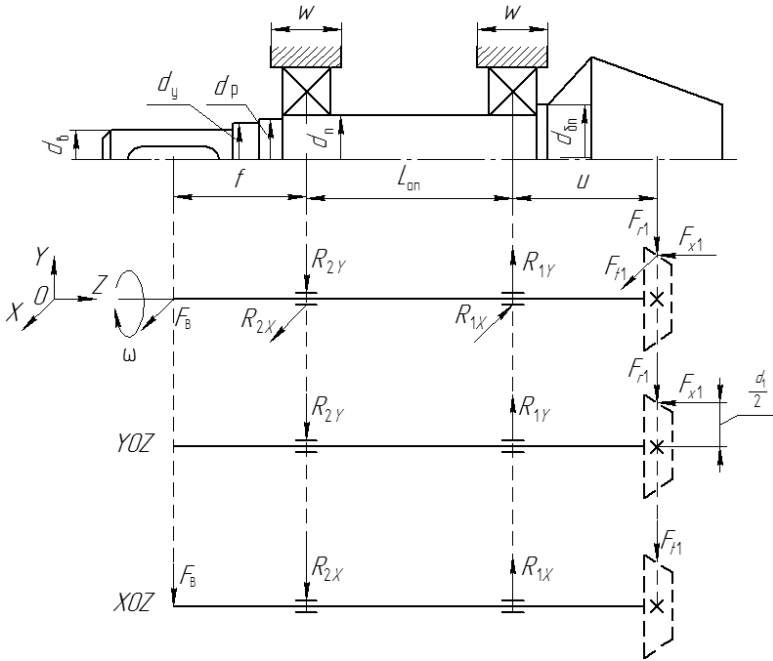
Схема нагружения быстроходного вала конического одноступенчатого редуктора
